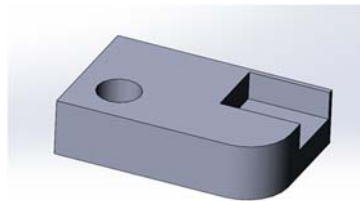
Тестова модель для перевірки точності розмірів при фрезеруванні
